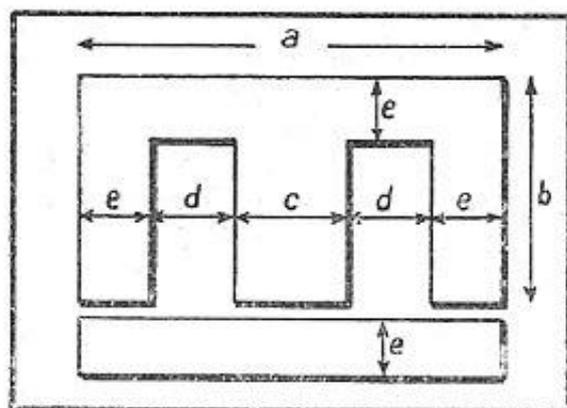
Forme générale et dimensions des tôles utilisées pour la construction des bobines d'inductance.
